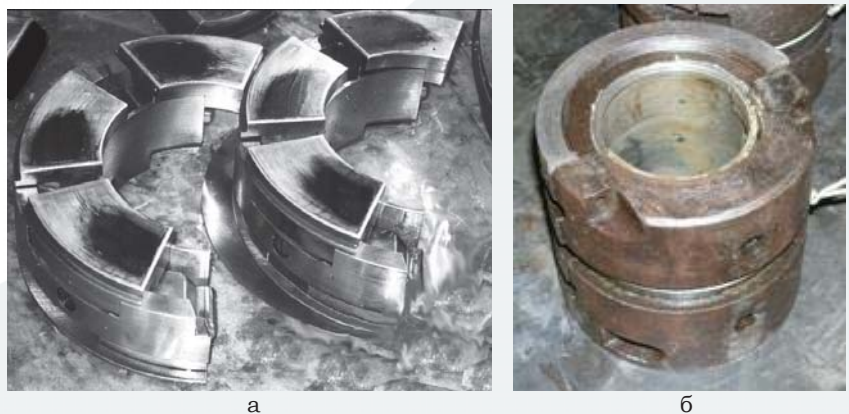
Изношенные поверхности упорных (а) и опорных (б) подшипников скольжения.
